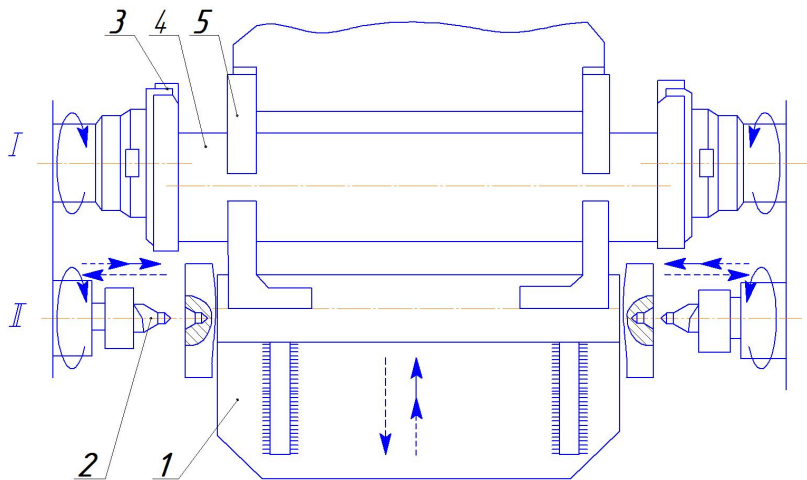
Двухпозиционный фрезерно-центровочный полуавтомат
